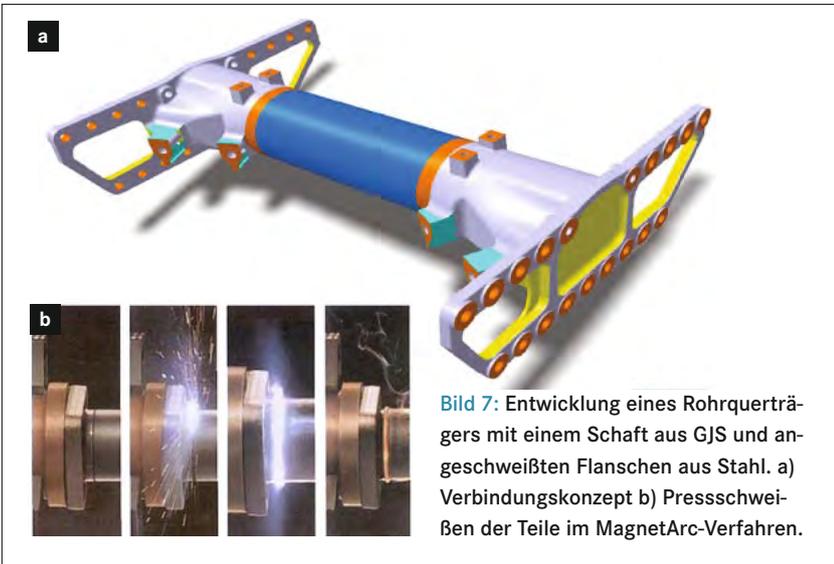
Entwicklung eines Rohrquerträgers mit einem Schaft aus GJS und angeschweißten Flanschen aus Stahl. a) Verbindungskonzept b) Pressschweißen der Teile im MagnetArc-Verfahren.
